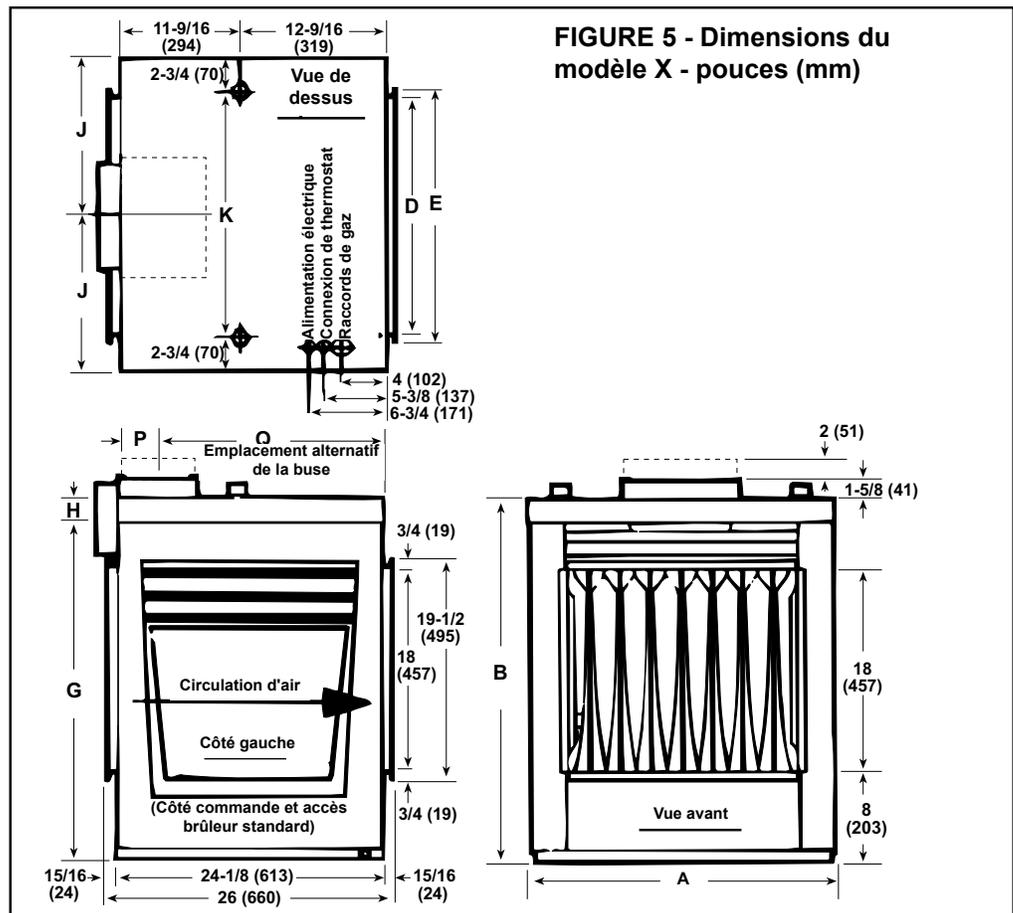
Dimensions du modèle X - pouces (mm)
